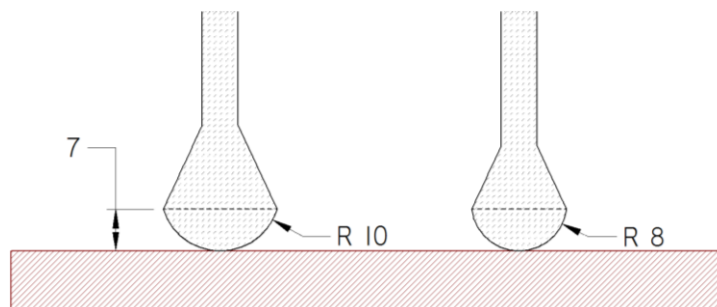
Pontas esféricas testadas (dimensões em milímetros).
